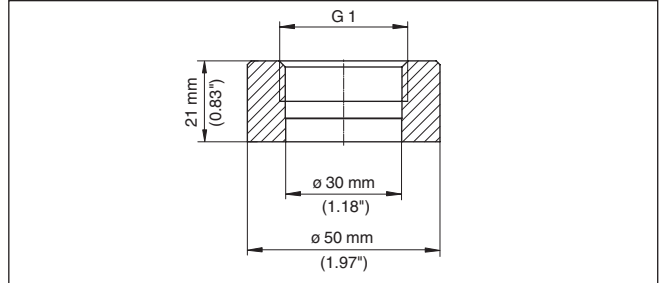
Maße Einschweißstutzen G1 (ISO 228-1) - VEGABAR 82, 83
